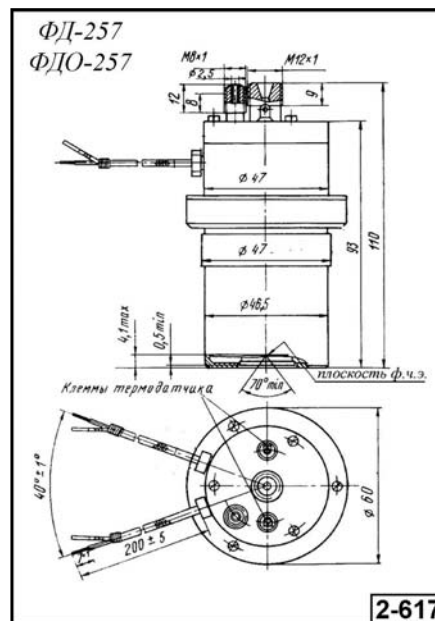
Внешний вид и габаритные размеры охлаждаемых фотодиодов ФД-257 и ФДО-257
